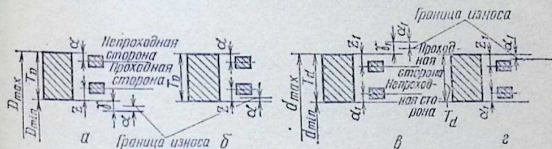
Схемы расположения полей допусков калибров для номинальных размеров свыше 180 мм:
